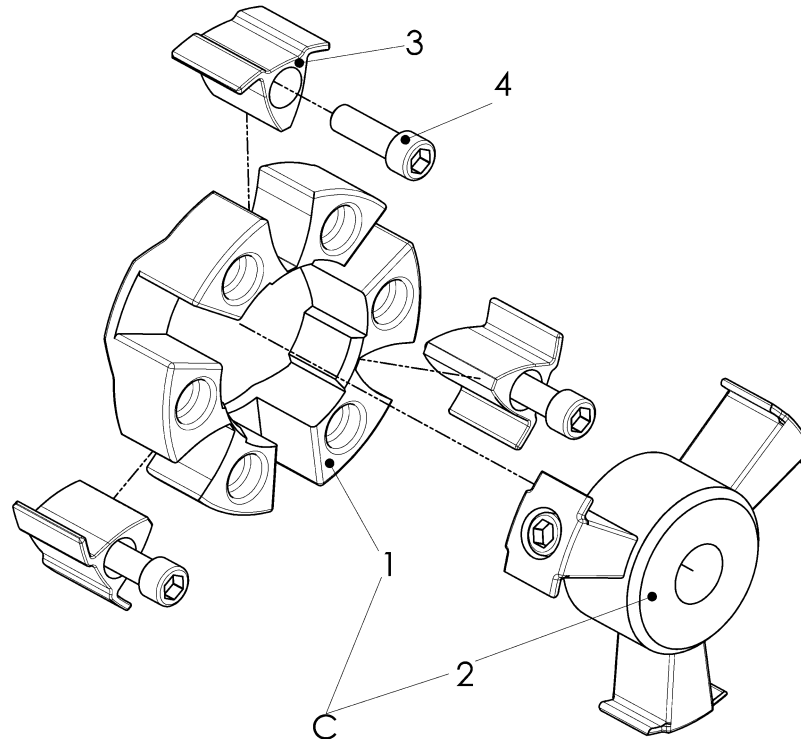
Vormontierte Baugruppe (C) für Erstmontage vorbereiten
